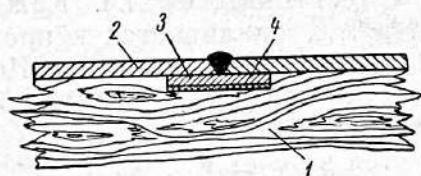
Установка прокладок в районе сварного шва.
